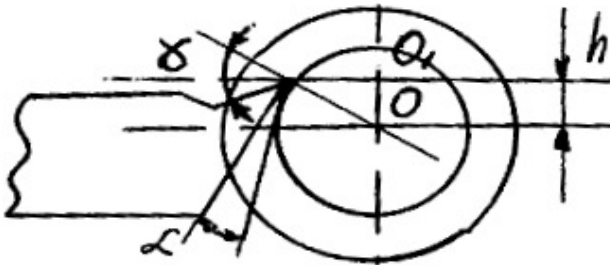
Розміщення вершини різця вище осі обертання заготовки при зовнішньому точінні
